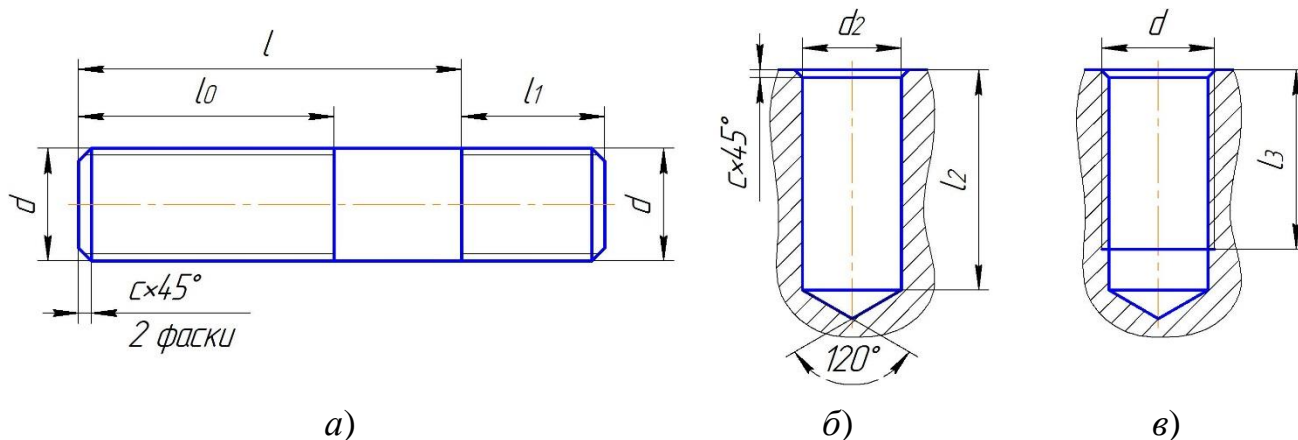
Параметры: а - шпильки; б - гnezда под резьбу; в - гnezда с резьбой
